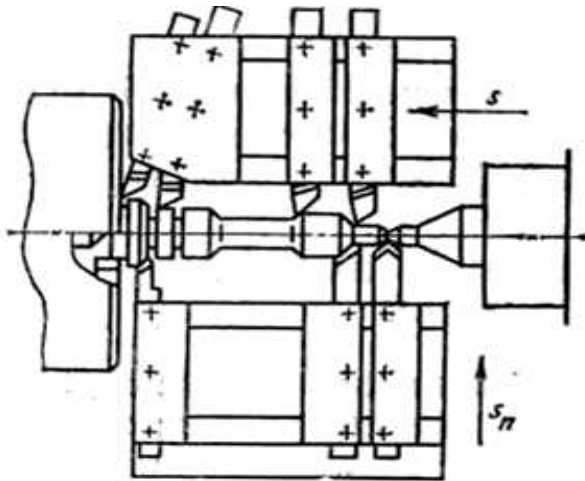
Схемы обработки с использованием многолезцовой наладки
